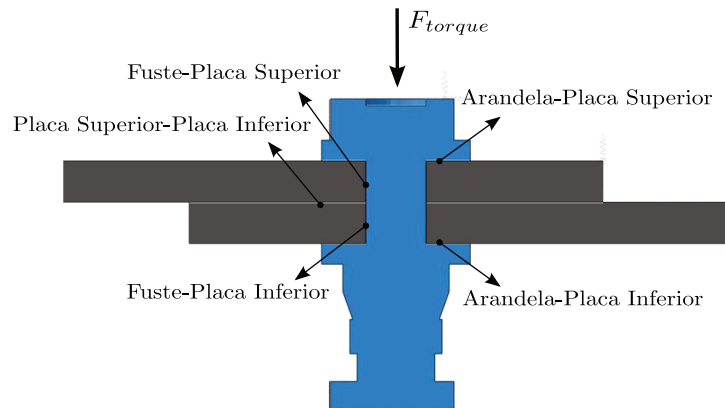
Partes en contacto en la unión y dirección de la fuerza de apriete.
